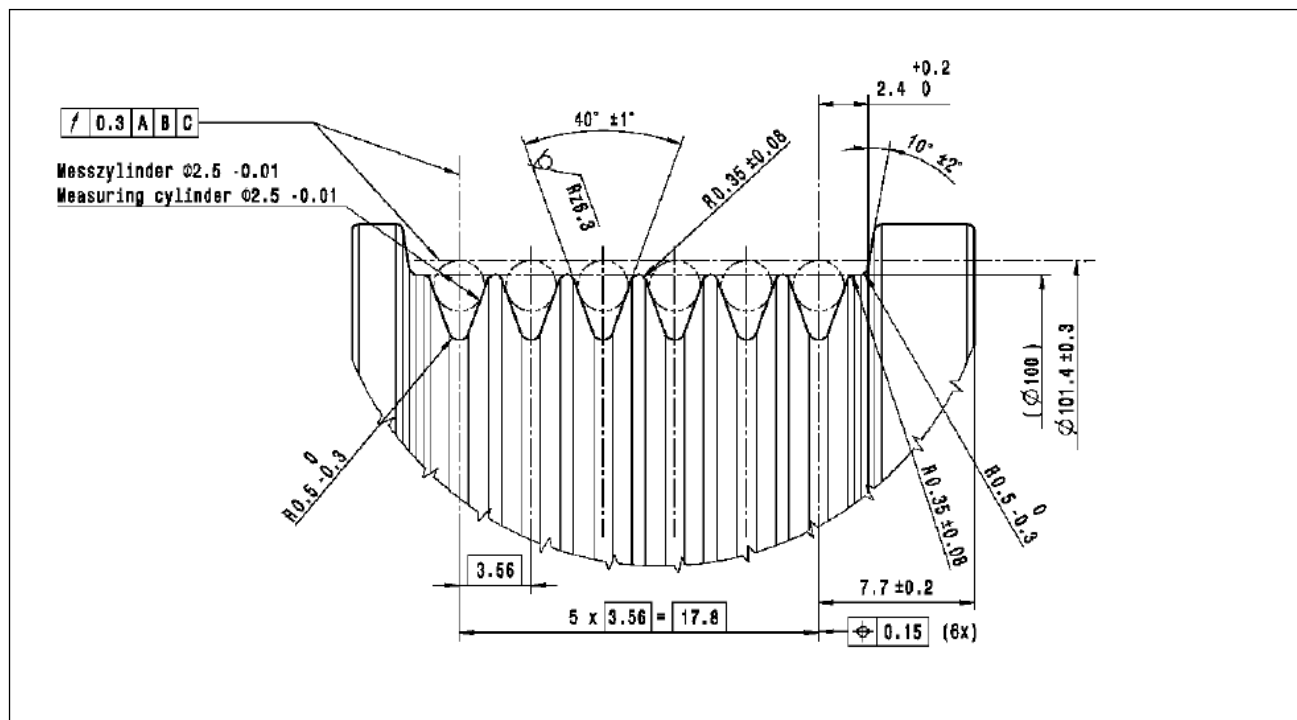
Детальное изображение U – Шкив компрессора климатической установки DENSO-75EU17
